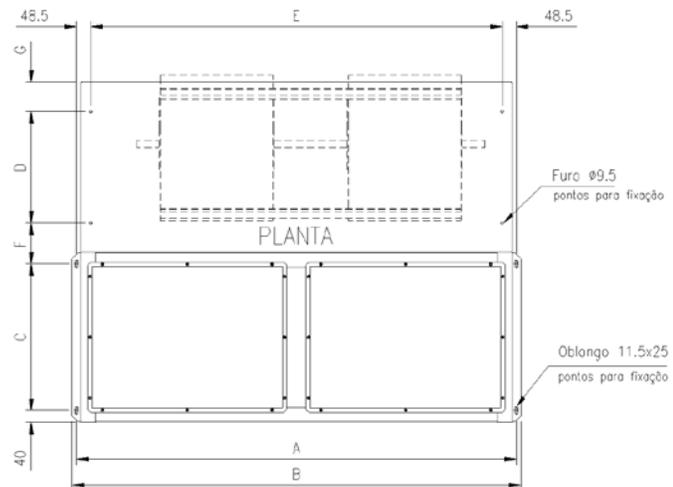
Dimensões para Fixação dos Módulos no Piso 050 a 500 - Gabinete Vertical
